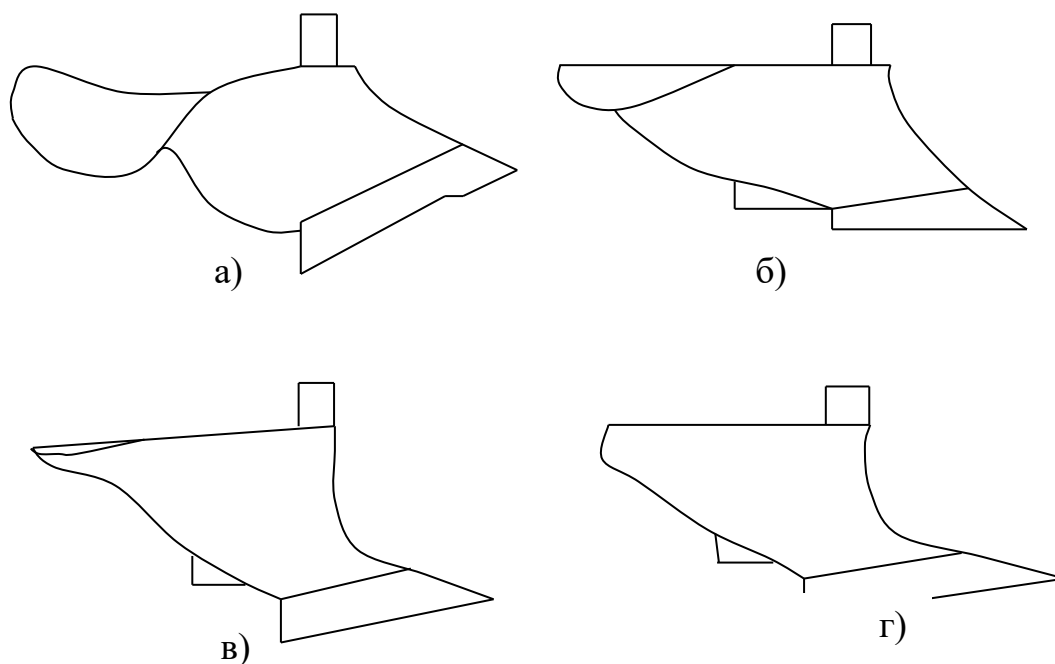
Схема форм рабочих поверхностей отвалов: а - винтовой; б - полувинтовой; в - культурный; г – цилиндрический
